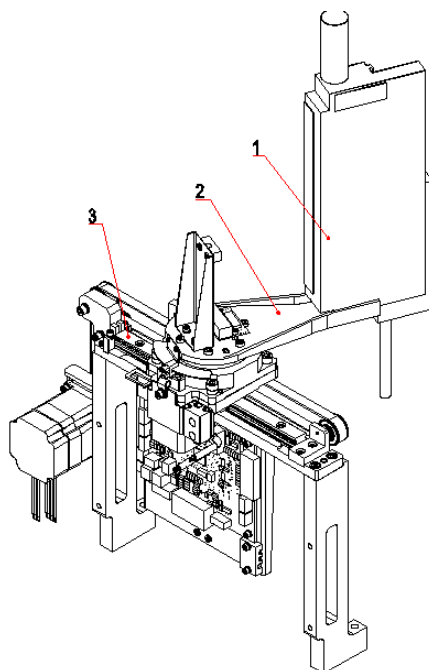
Схематический чертеж держателя пробоотборника
